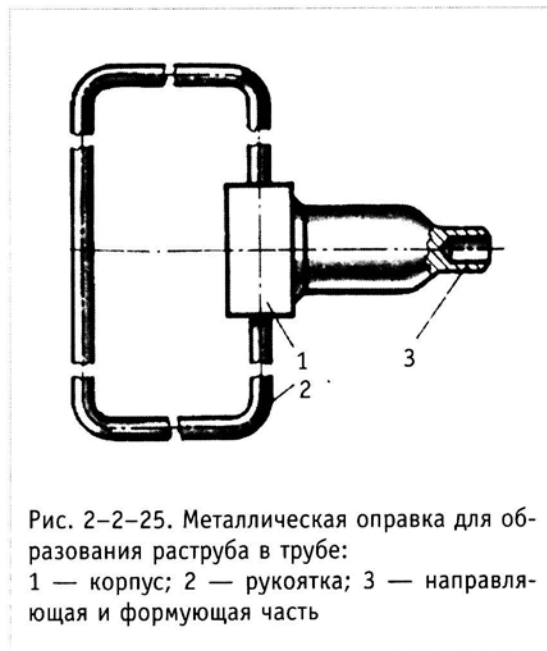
Металлическая оправка для образования раструба в трубе: 1 — корпус; 2 — рукоятка; 3 — направляющая и формирующая часть
